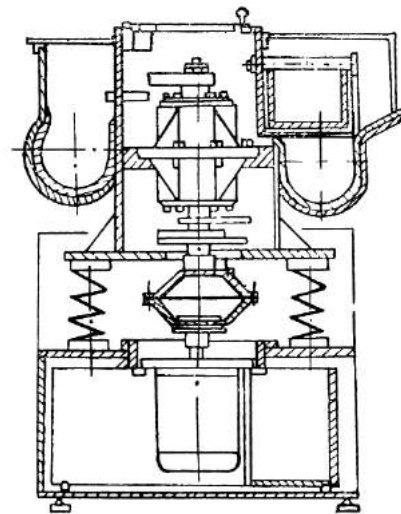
Схема галтовочного станка с торообразной рабочей камерой [5]
